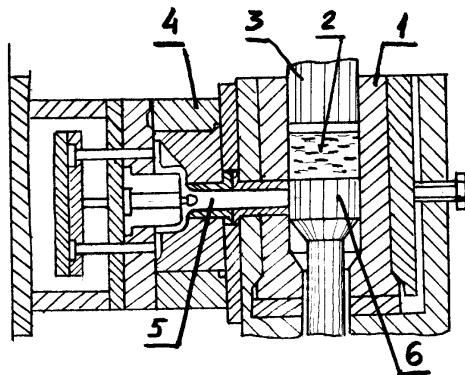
Схема литья под давлением с вертикальной камерой прессования.
